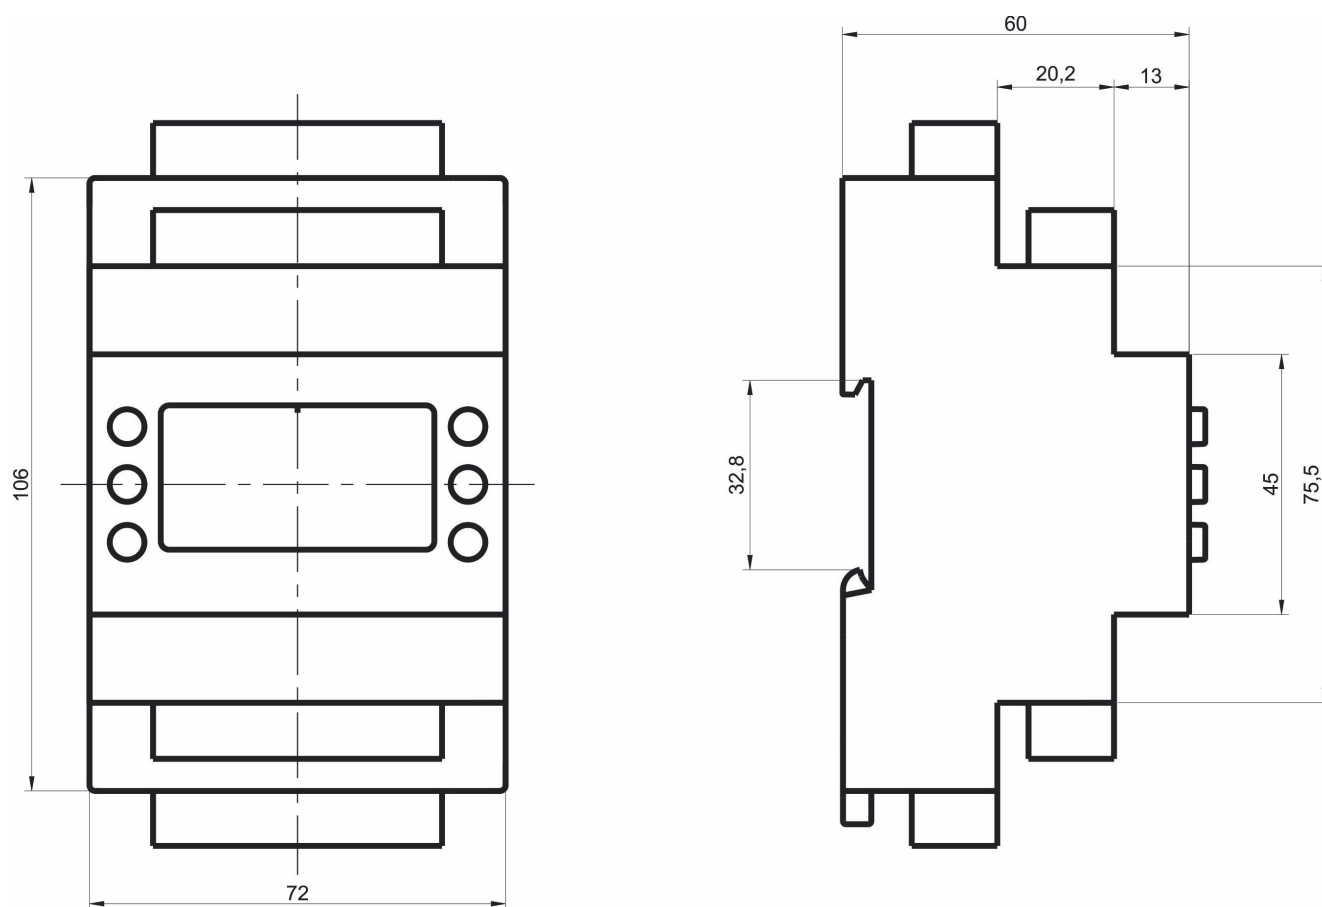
Габаритные и установочные размеры модуля ЦПУ
